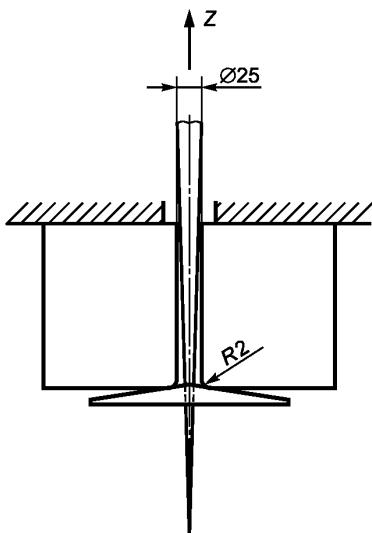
Схема испытания прочности крепления опорного элемента в направлении действия растягивающего усилия
